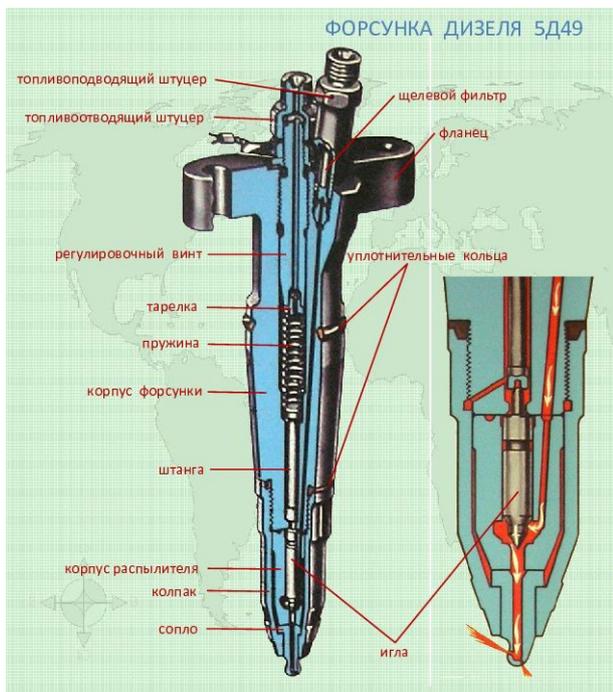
Общий вид форсунки дизеля 8ЧН 26/26
